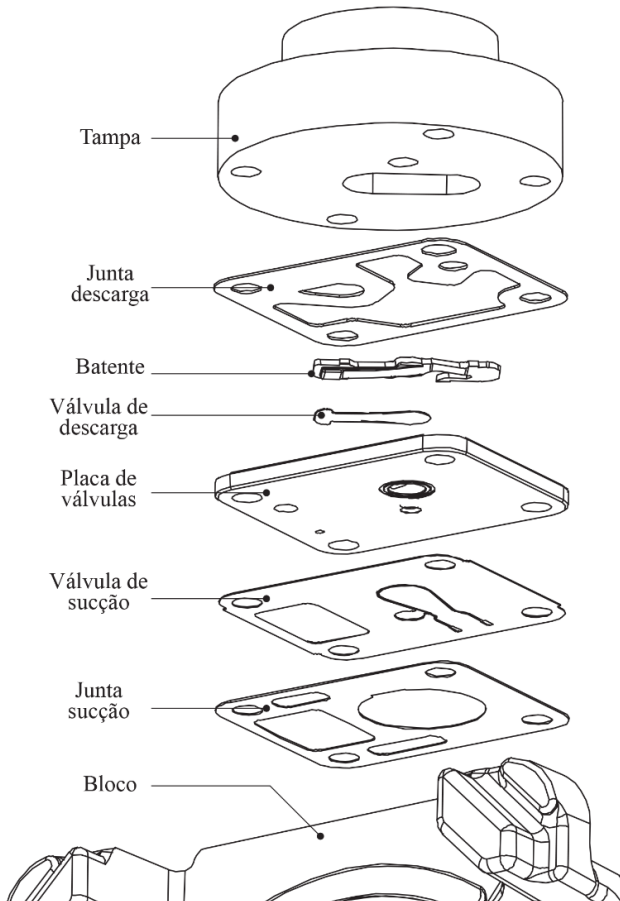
Vista explodida dos elementos do kit do compressor.
